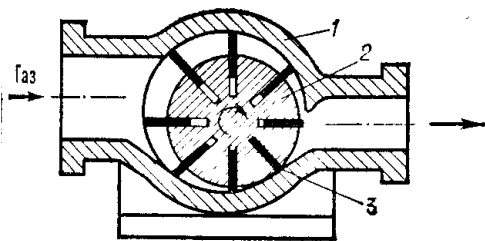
Схема ротационного компрессора: 1 — цилиндр; 2 — ротор; 3 — пластины.
